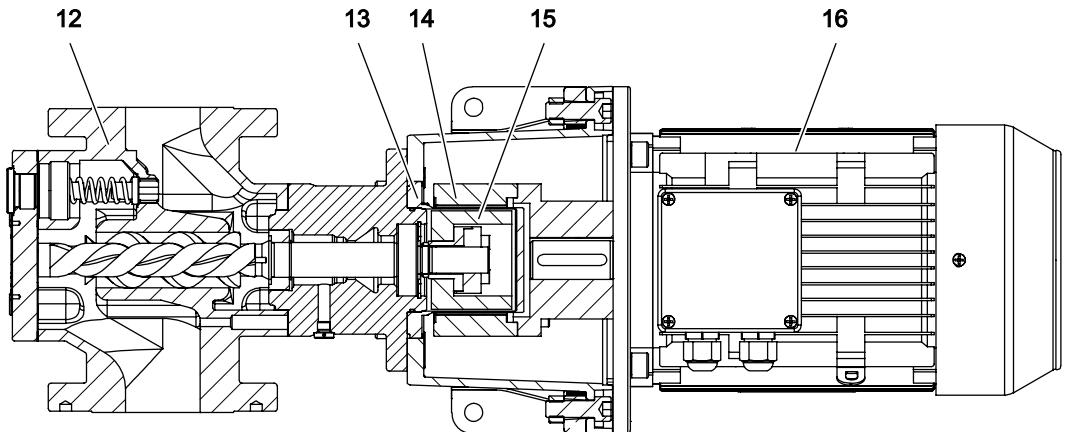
Aufbau Pumpenaggregat – Prinzipbild
